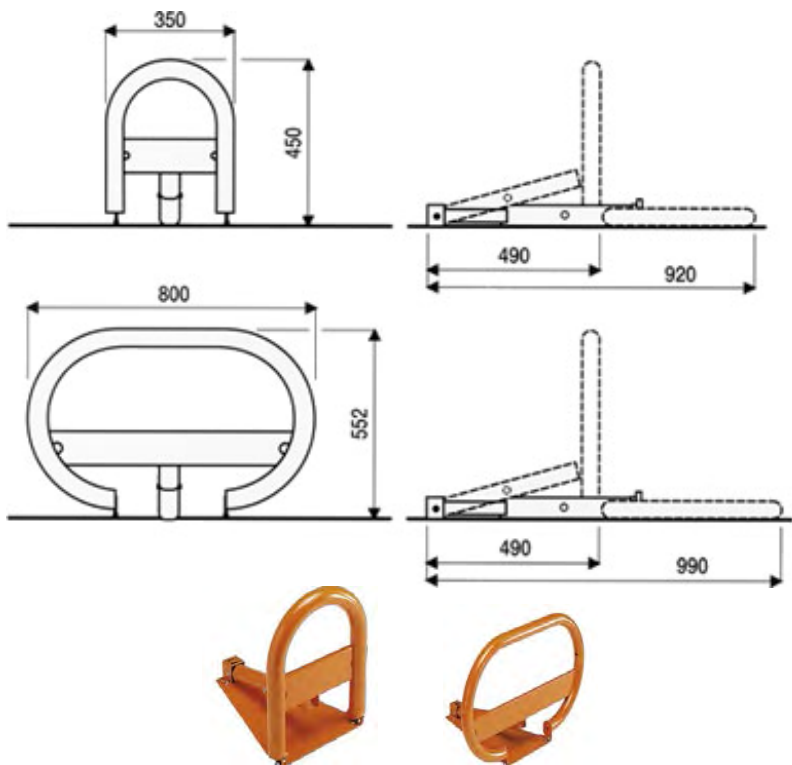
Размеры и внешний вид автоматической системы для резервирования парковочного места
